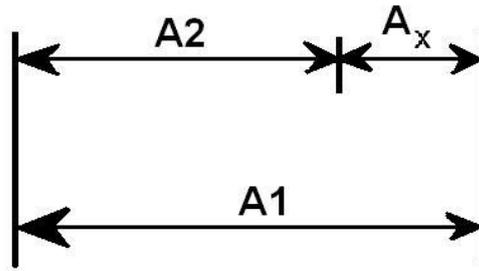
Схема размерной цепи для расчёта замыкающего звена
